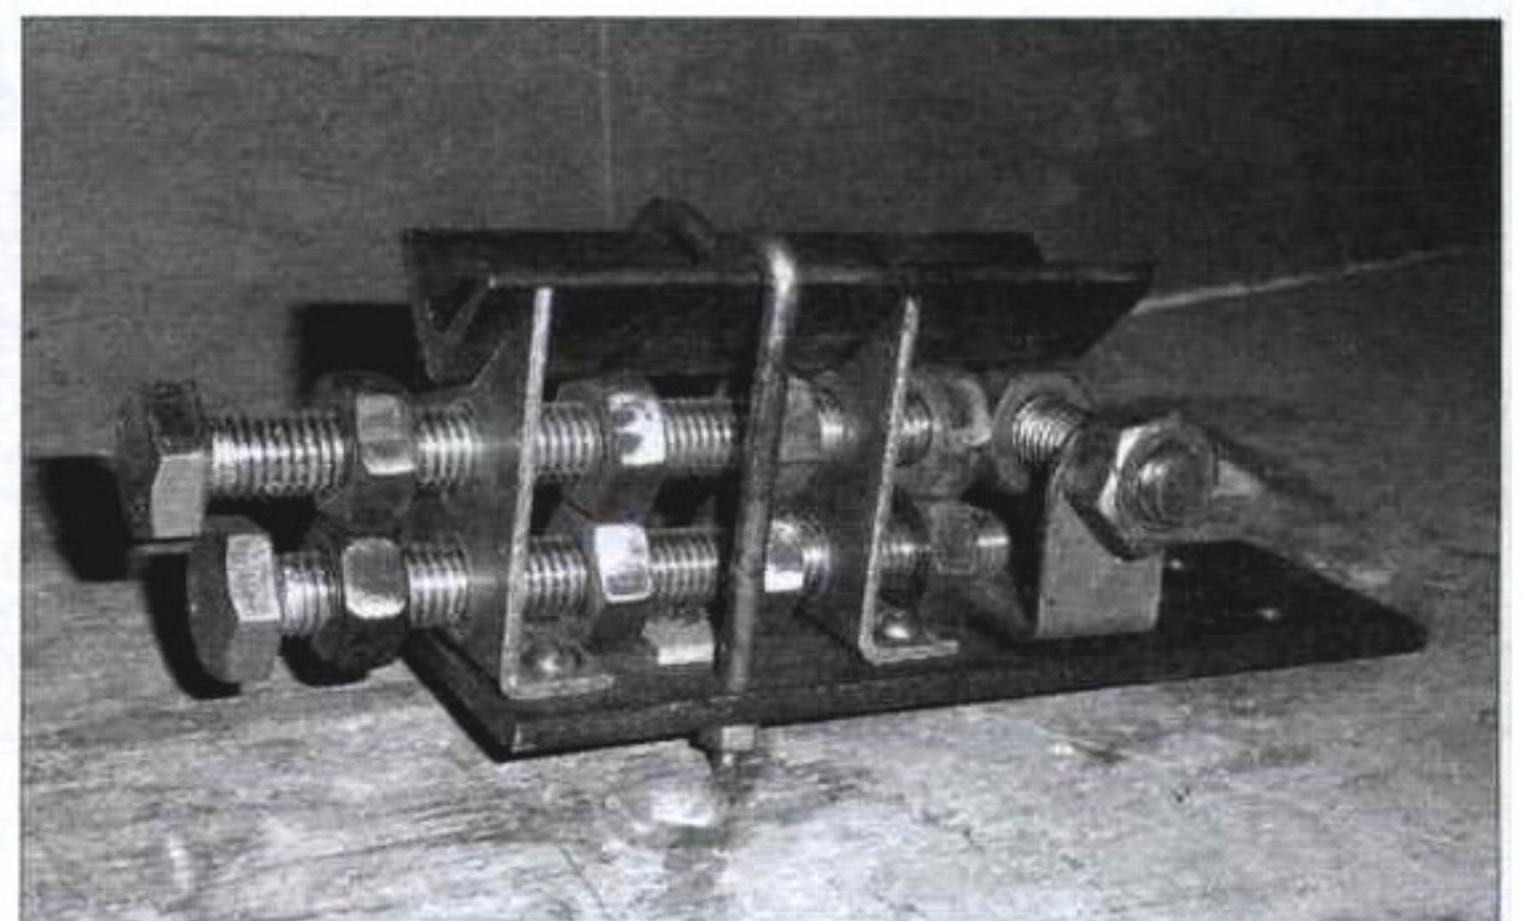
Кондуктор в сборе (подготовлен к сварке)
